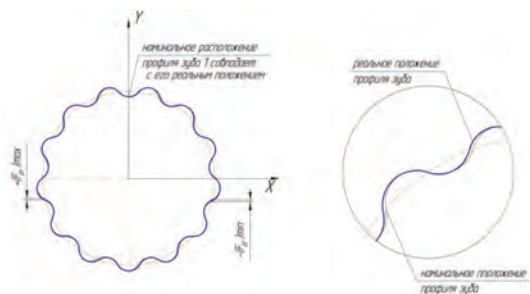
Профиль сателлита планетарно - цевочного редуктора.
